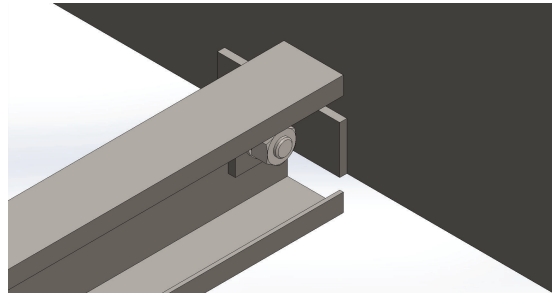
Unión soldada entre las vigas del aislante y un ángulo (Fuente propia)
